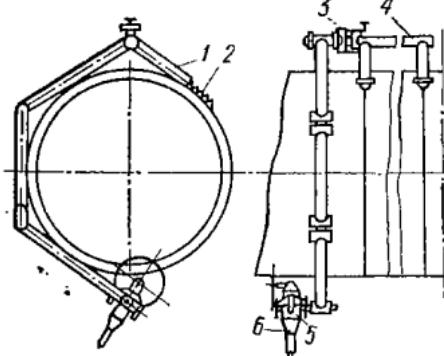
Устройство для резки пластмассовых труб большого диаметра:
